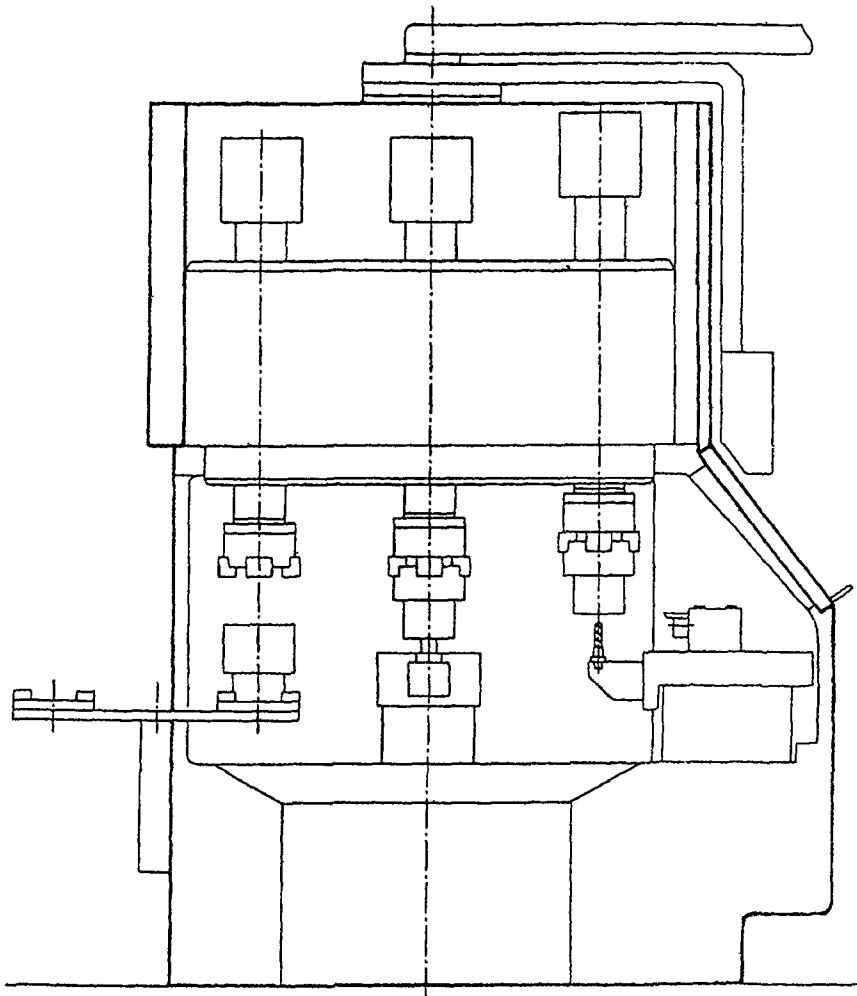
с — Вертикальний багатошпindelний патронний токарний верстат з цифровим програмним керуванням
